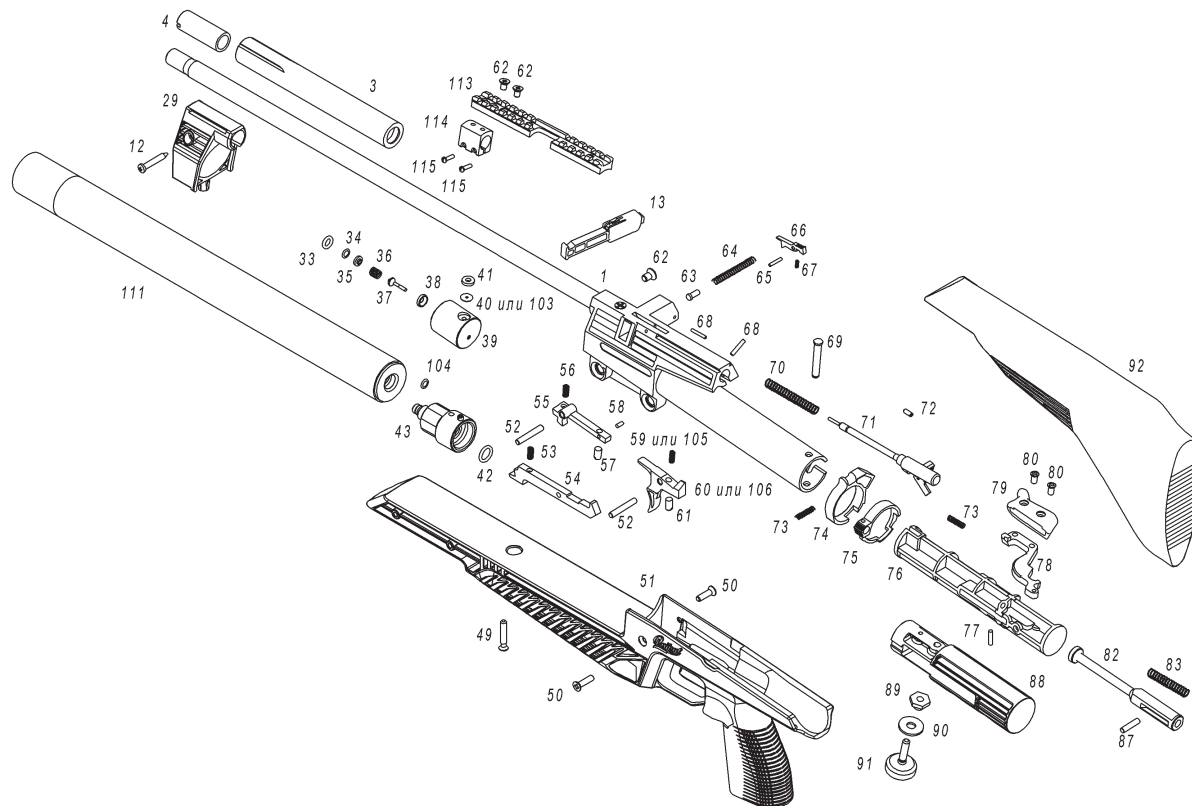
Сборочные единицы и детали винтовок МР-55К, МР-55КС с планкой под прицел
